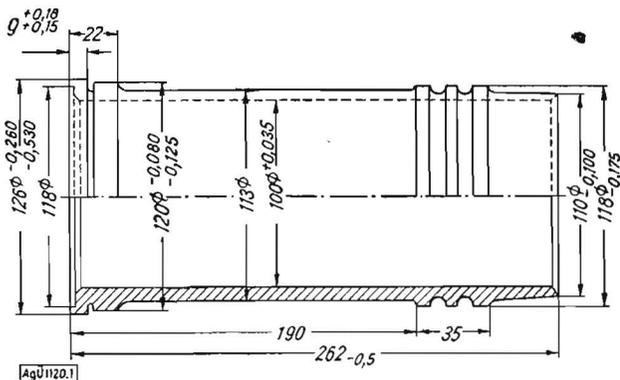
Buchse des Zylinderblocks vom Motor des Traktors KD-35
